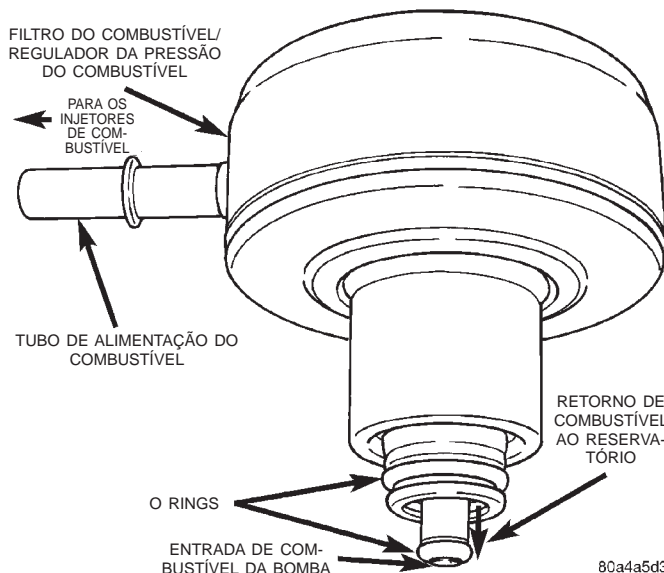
Gaxeta do Filtro do Combustível/Regulador da Pressão do Combustível
